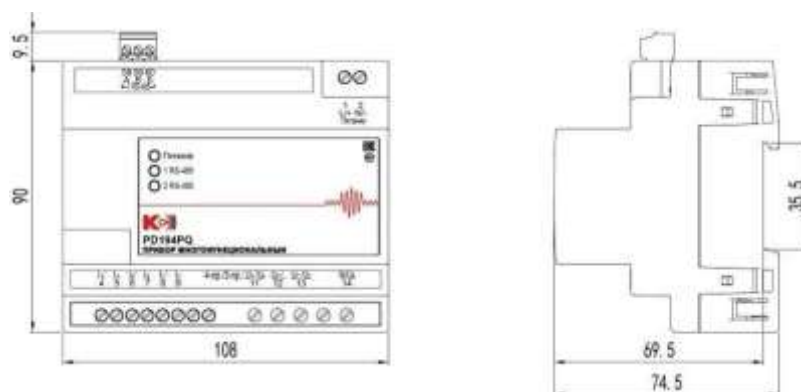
Внешний вид и размеры прибора PD194PQ-7K0T-00001
